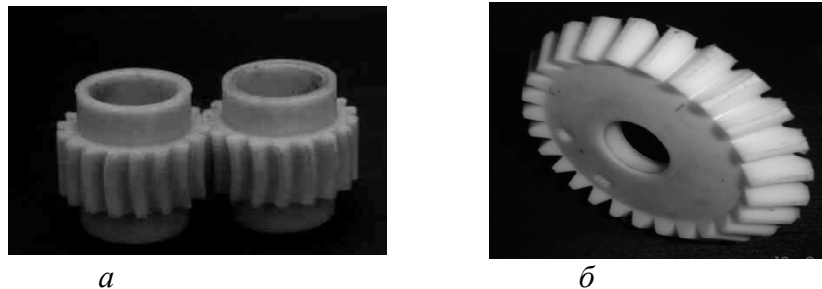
Типи зубчастих коліс, нарізаних однією дисковою фрезою на зубофрезерному верстаті
